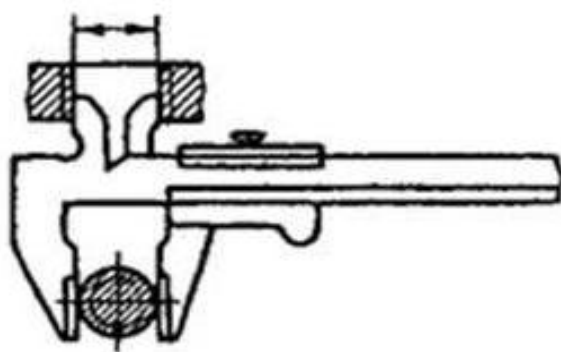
Определение диаметра резьбы с помощью штангенциркуля
